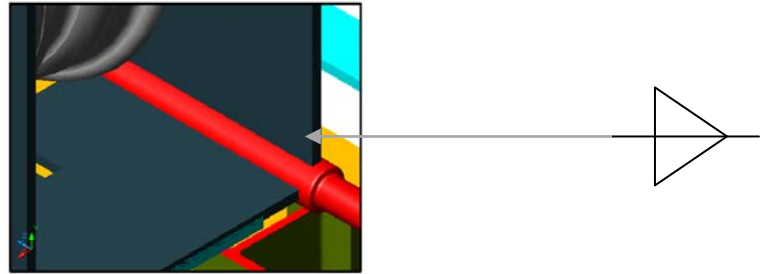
SOLDADURA EN EL EJE
